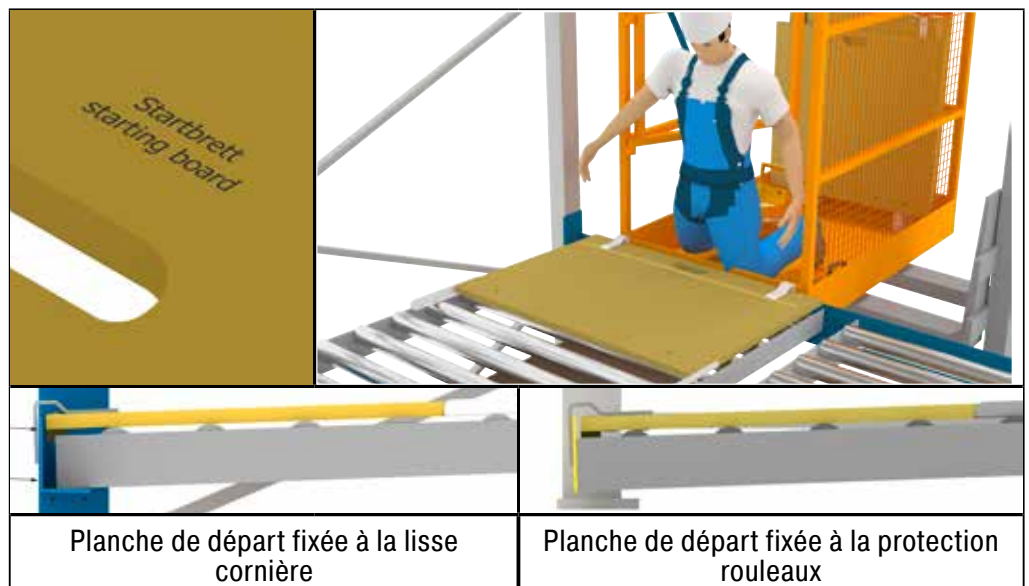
Placer la planche de départ BITO dans le couloir voisin.
